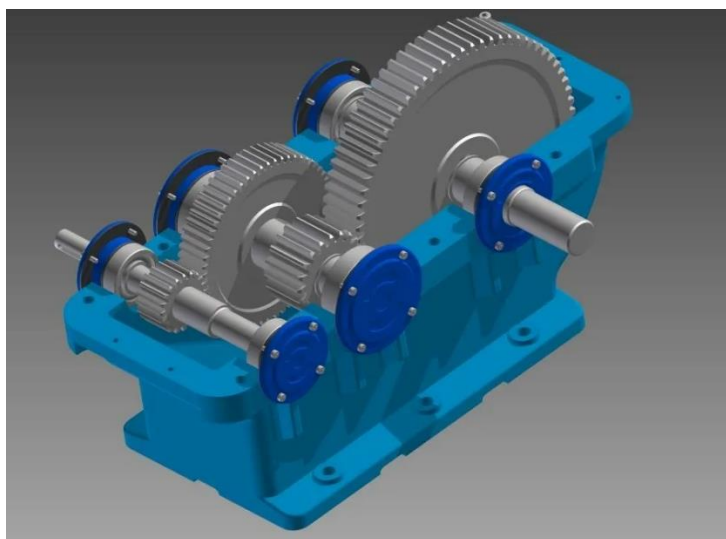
Редуктор цилиндрический трехступенчатый РЦШ-1300 (3D изображение)
